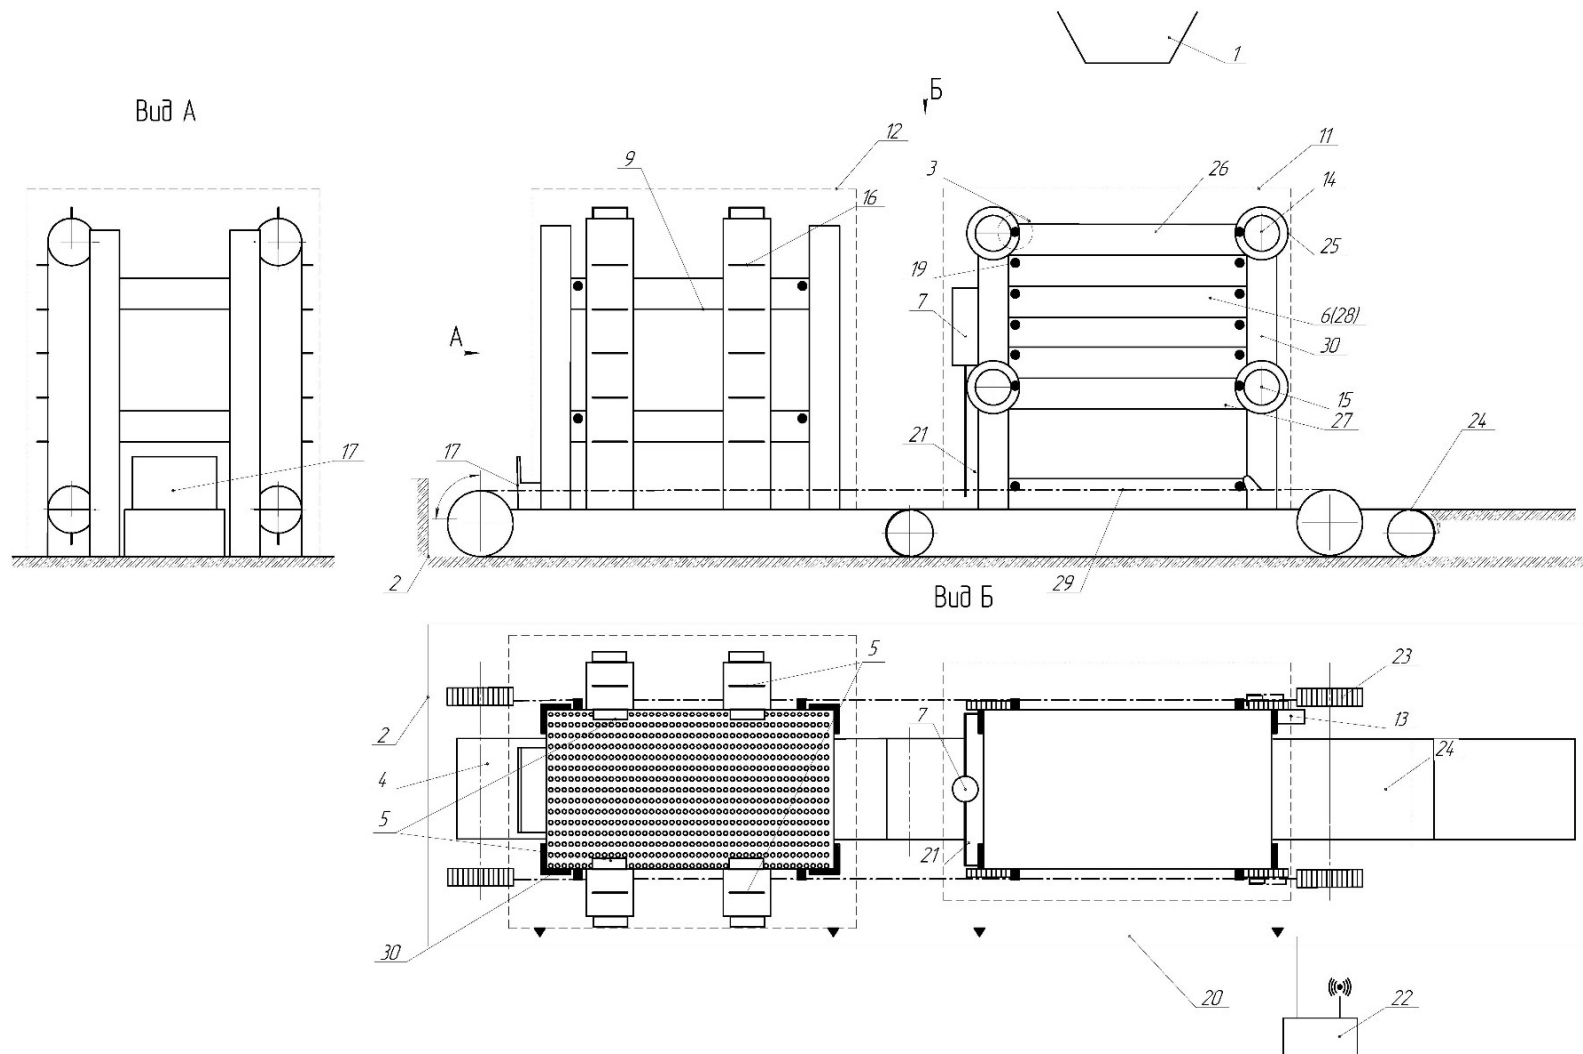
Схема устройства установки обезвоживания торф, где 1 – дозировочный бункер; 2 – станина с направляющими; 3 – приводной механизм передачи поддонов; 4 – горизонтально-подвижный питатель с приводами; 5 – подъемник поддонов; 6 – поддон; 7 – вертикально подвижный пригруз; 11 – колодец спуска; 12 – колодец подъема; 13 – средства отвода влаги; 14 – привод удержания; 15 – привод выпуска; 16 – механизм подъема поддонов с приводом; 17 – ограничитель движения поддонов; 20 – датчики перемещения; 21 – шибер очистки поддона; 22 – блок управления; 23 – крюк с приводом; 24 – конвейерная лента с приводом; 25 – цевочное колесо с приводом; 26 – верхний поддон; 27 – нижний поддон; 28 – столб вложенных поддонов; 29 – выпущенный поддон; 30 – вертикальные направляющие
